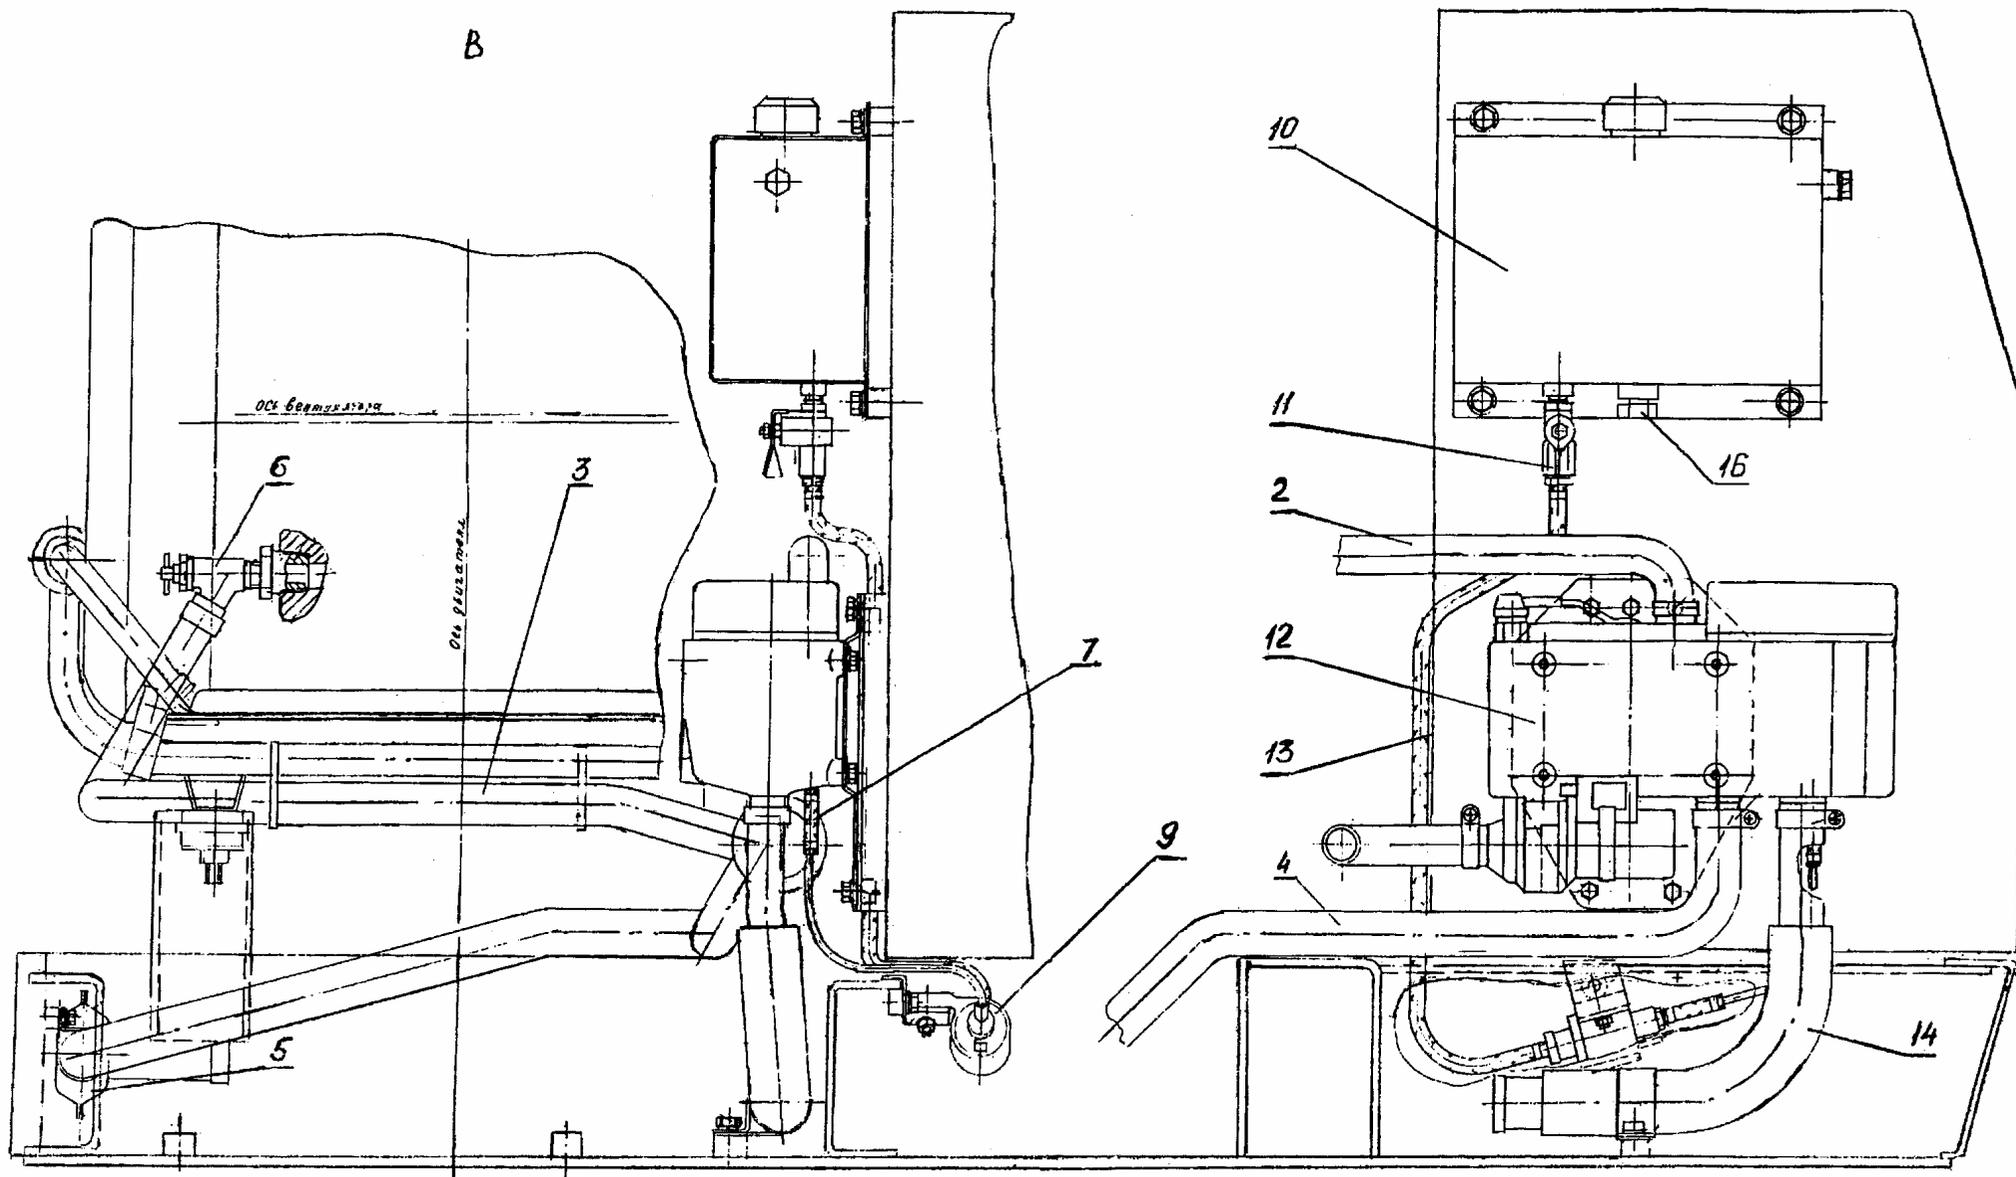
Установка предпускового подогрева двигателя и отопления кабины
